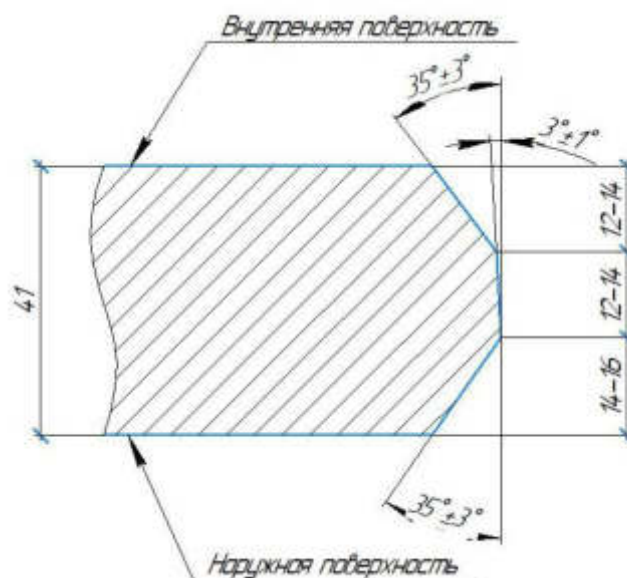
Общий вид подготовки кромки под сварку продольного шва
